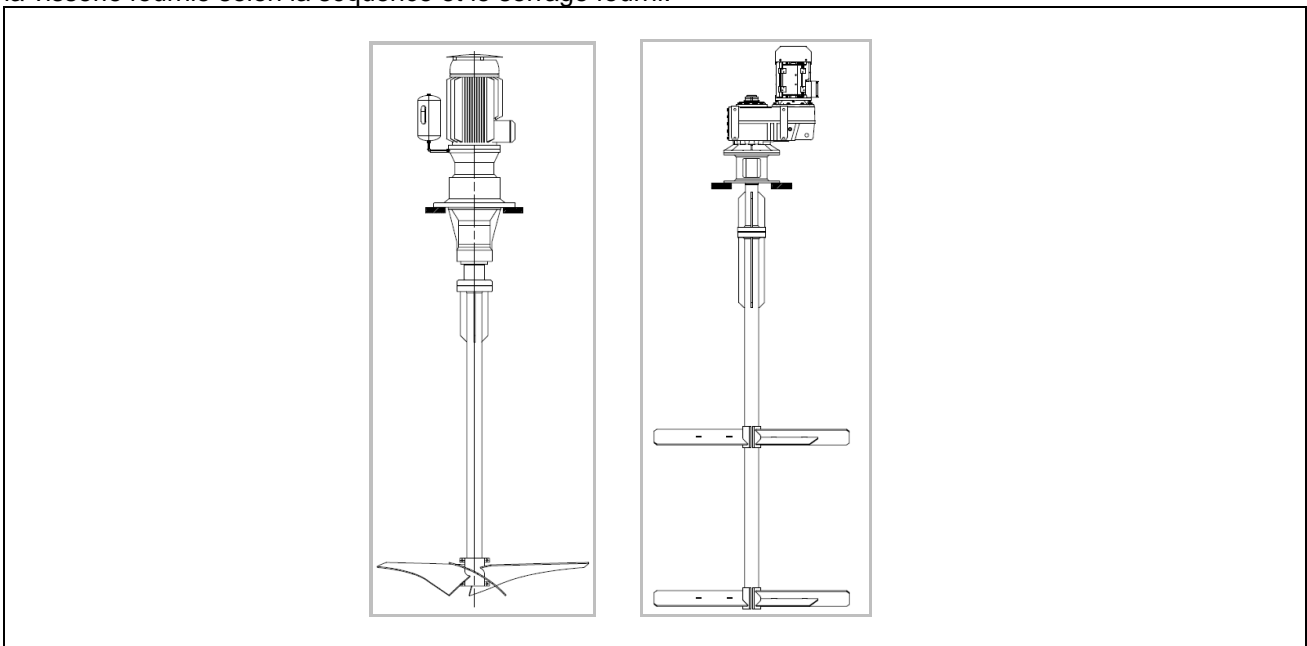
Agitateur non- assemblé et joint à bride: vues
